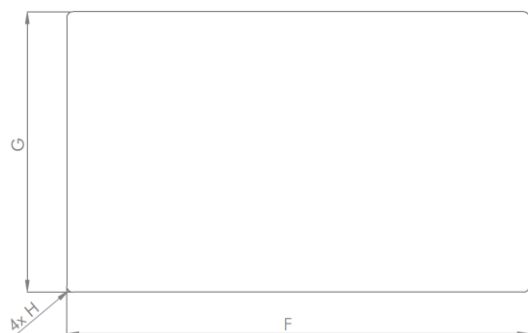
Dimensionen Open Frame Ausschnitt Gegenplatte
